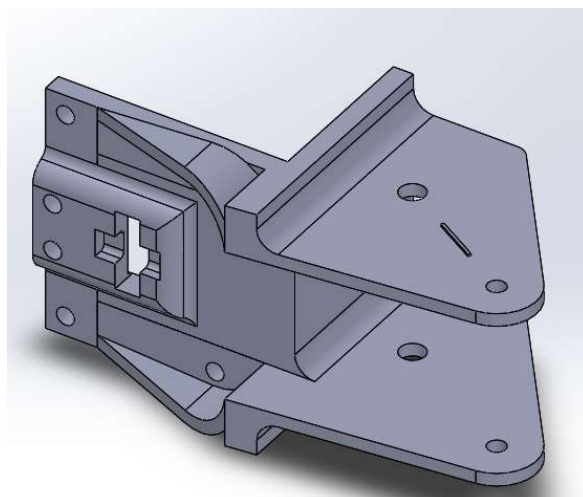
Unión viga central-viga lateral-brazo vista detallada
